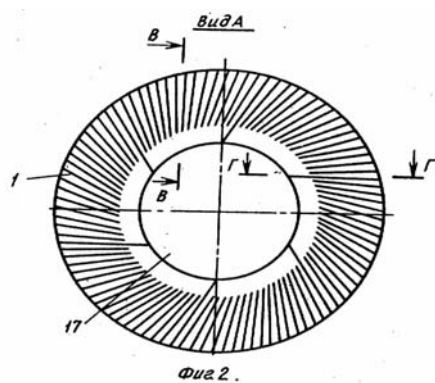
Рабочая поверхность с радиальными канавками [4]
